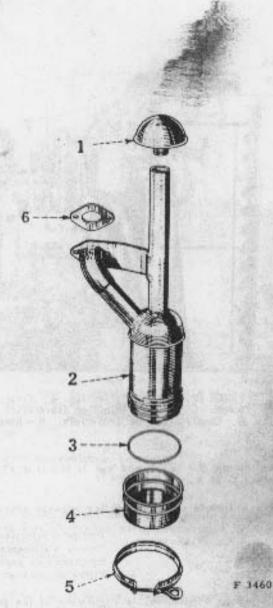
Filtre à air. I - Chapeau. 2 - Corps de filtre. 3 - Joint. 4 - Bol à huile. 5 - Collier de fixation du bol. 8 - Joint de bride sur collecteur d'admission.
